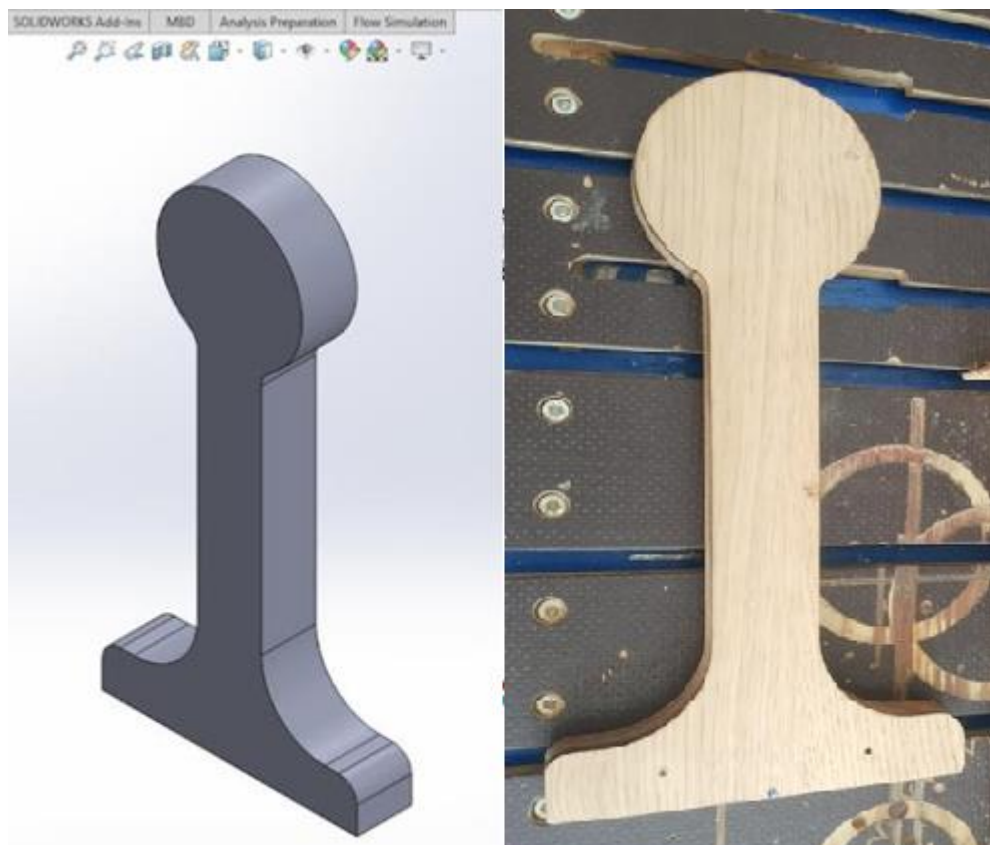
3D-модель елемента стійки корпусу та готовий виріб
